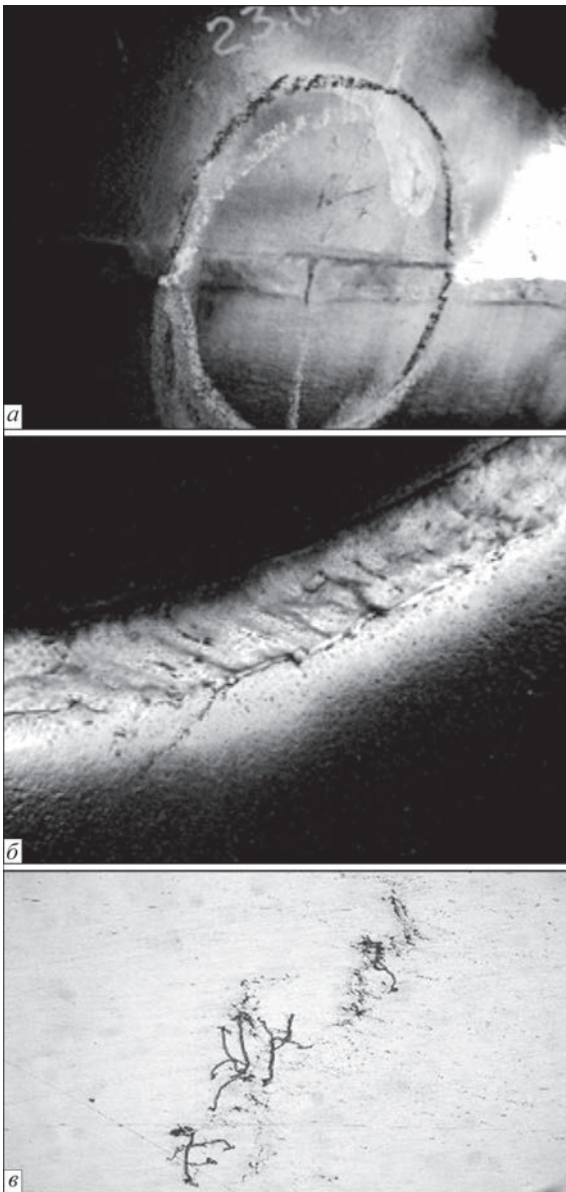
Макро- (а, б) и микротрещины (в), образовавшиеся на внутренней (а) и внешней (б) поверхностях сварных соединений
